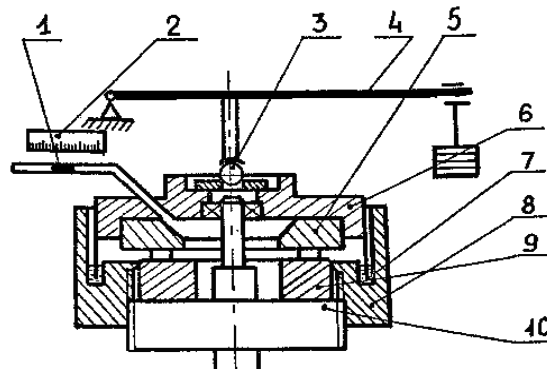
Устройство для измерения расхода воздуха: 1 – капля жидкости; 2 – расходомерная шкала; 3 – шаровая опора; 4 – рычаг; 5 – образцы; 6 – оправка; 7 – гидравлический затвор; 8 – прижимная гайка; 10 – шпindel
